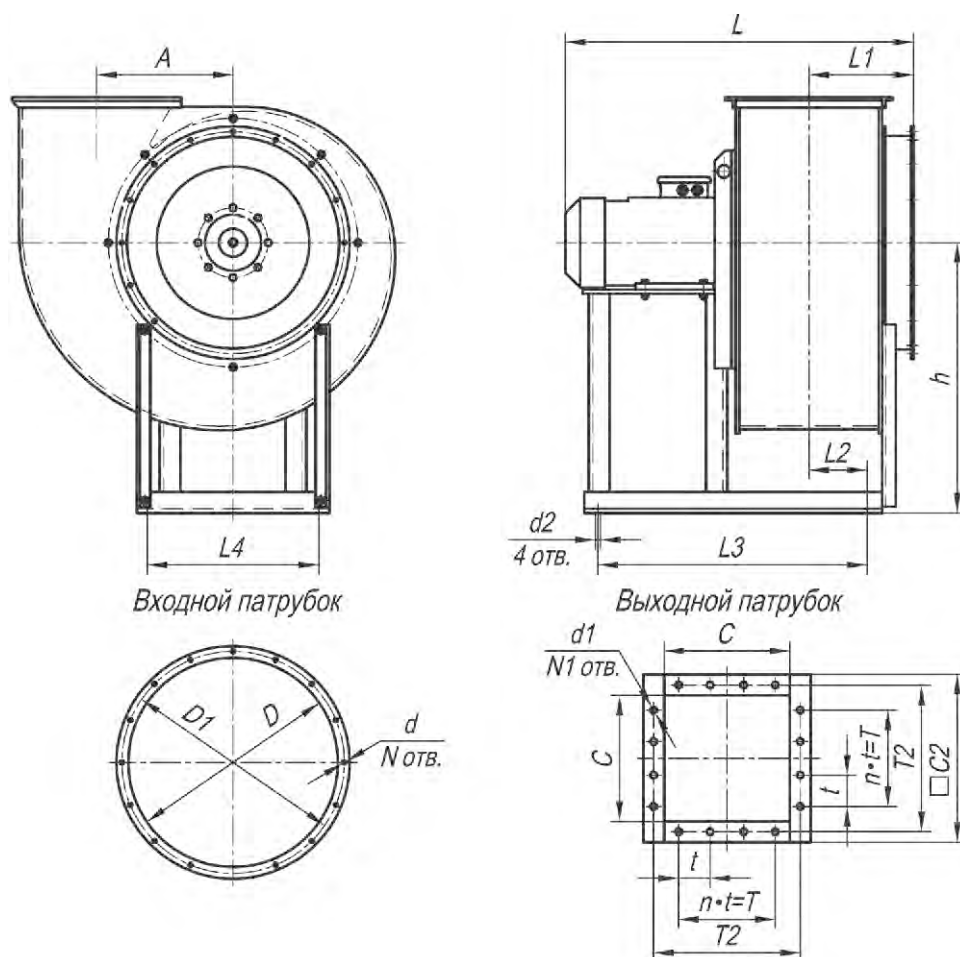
Габаритные и присоединительные размеры вентиляторов радиальных ВР 280-46 ДУ исп-1.
